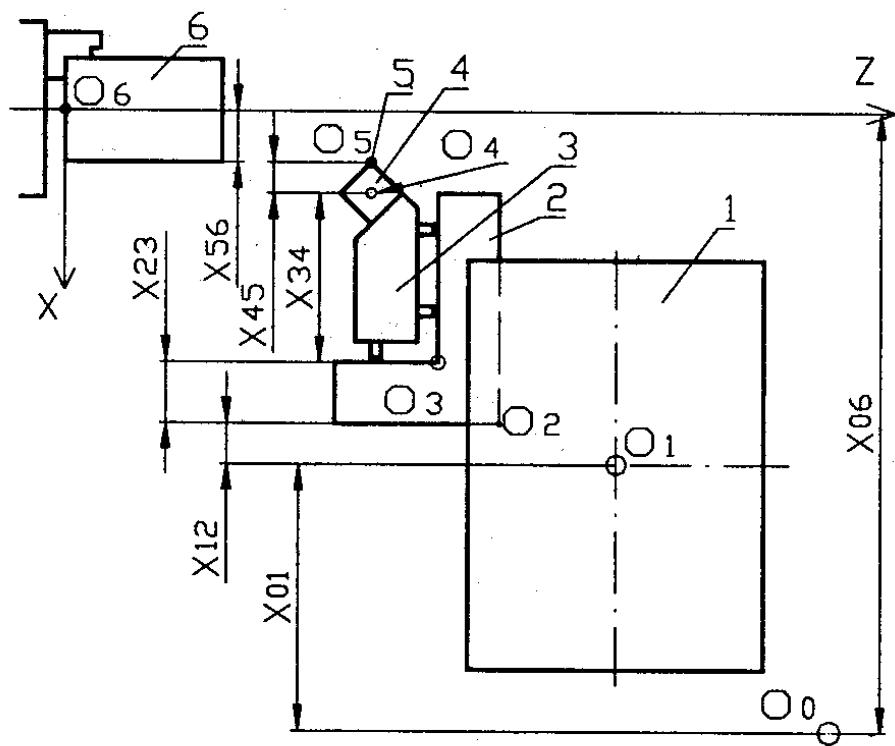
Размерная цепь наладки для токарного станка с ЧПУ
